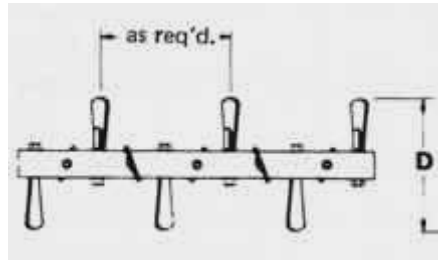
Tornillo de paletas. Fuente: <http://www.kwsmfg.com/services/screw-conveyor-engineering-guide/conveyor-flight-pitch-types.htm>
